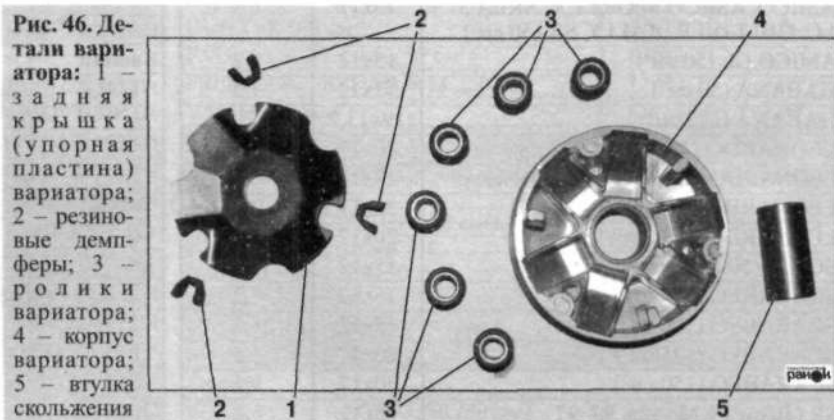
Детали вариатора: 1 – задняя крышка (упорная пластина) вариатора; 2 – резиновые демпферы; 3 – ролики вариатора; 4 – корпус вариатора; 5 – втулка скольжения
